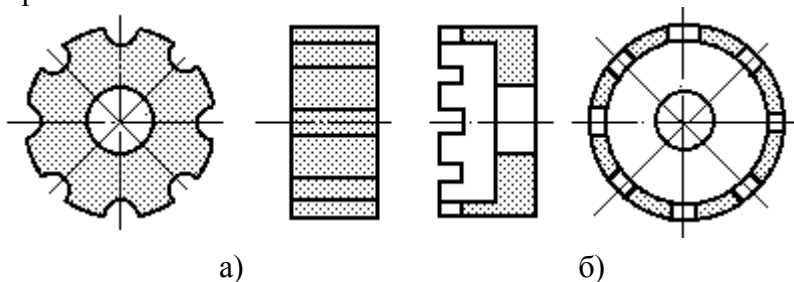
Круги с прерывистой рабочей поверхностью: а) - прямыми пазами; б) - с пазами на торце
